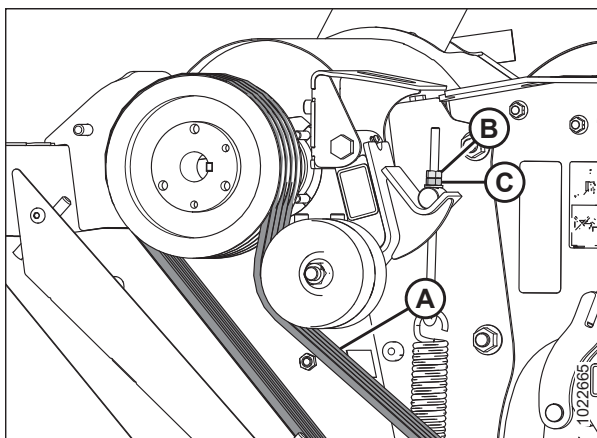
Contre-écrou et écrou de réglage du côté gauche du type tracté à disques rotatifs
